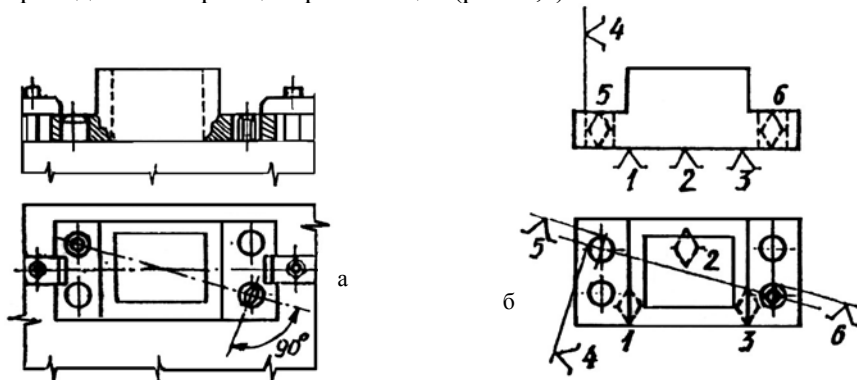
Пример установки заготовки в приспособлении (а) и теоретической схемы базирования (б)
